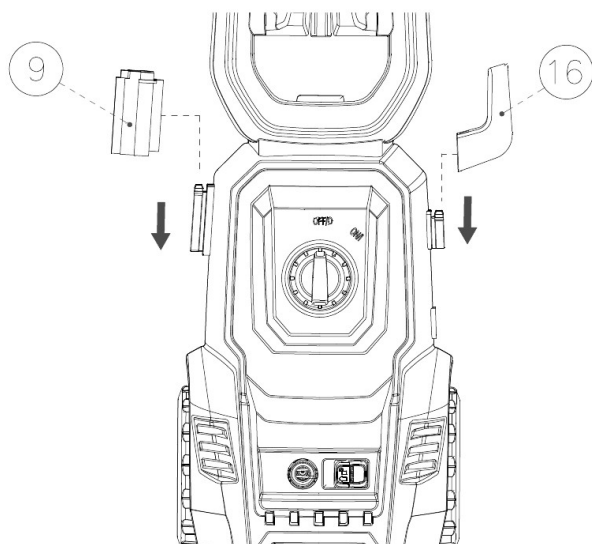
Montaje del soporte de la pistola y del soporte del cable
